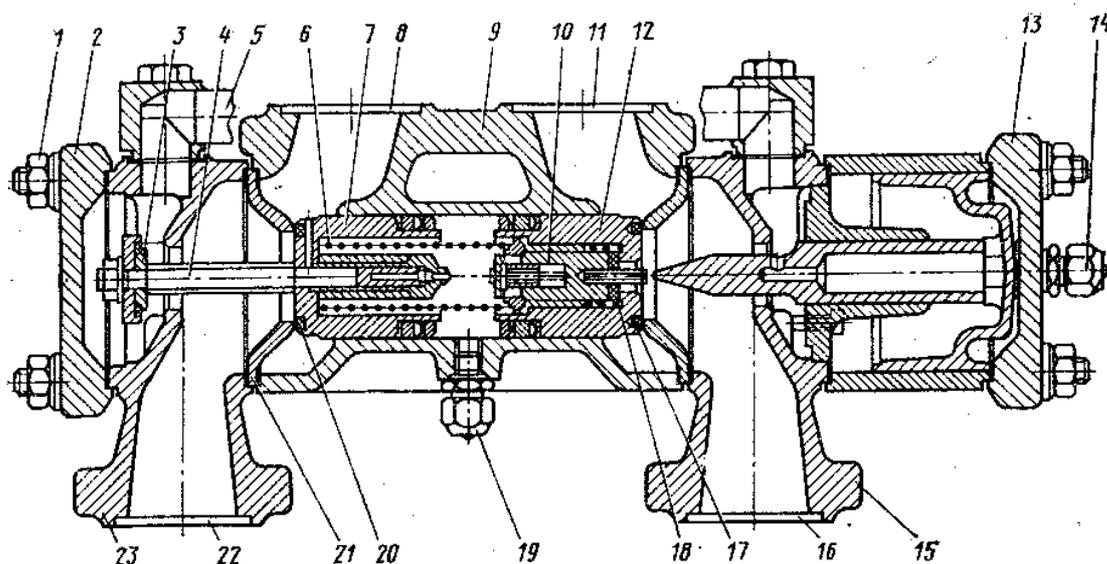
Автоматический запорный клапан компрессора холодильного агрегата FAL-056/5
